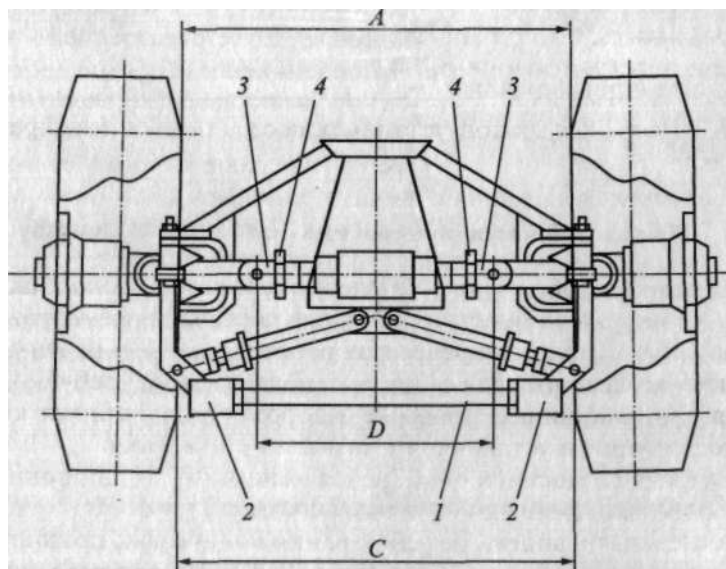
Регулировка схождения и развала колес автогрейдера:
